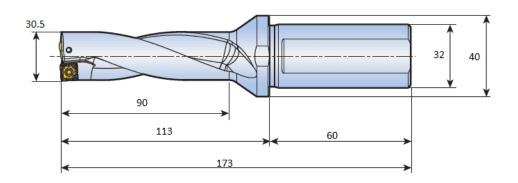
Сверло ТОР 3305-32Т2-09
